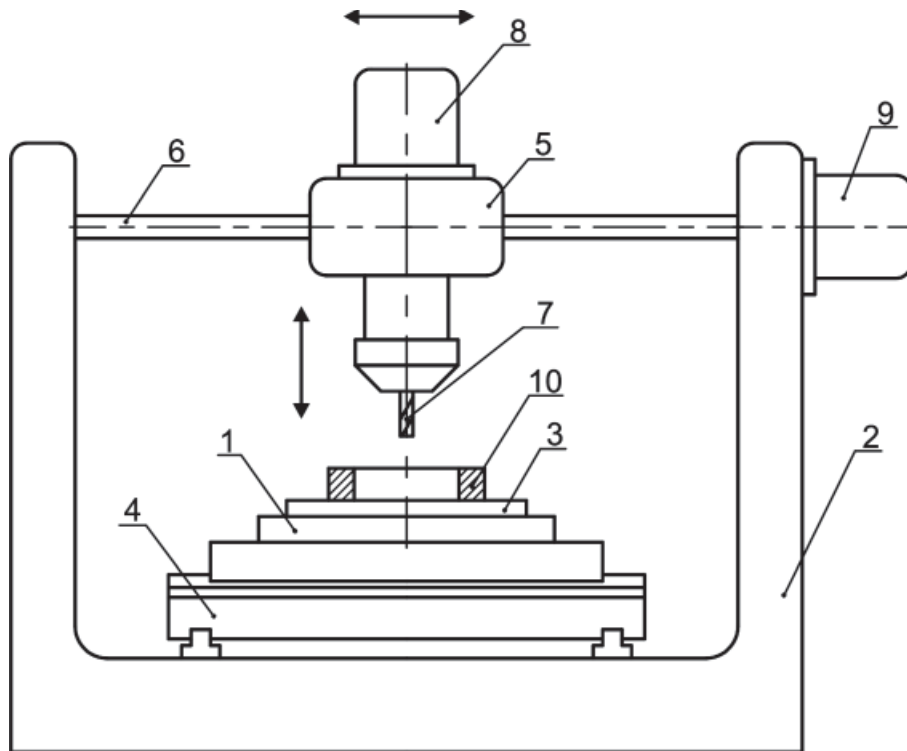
Схема технологического оборудования для обработки зубчатых венцов жёстких колёс методом обкатки:
